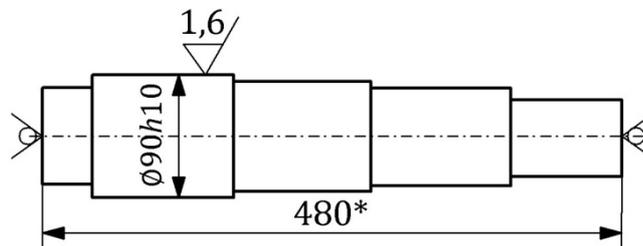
Схема полів допусків зовнішньої поверхні деталі за умов механічного оброблення
